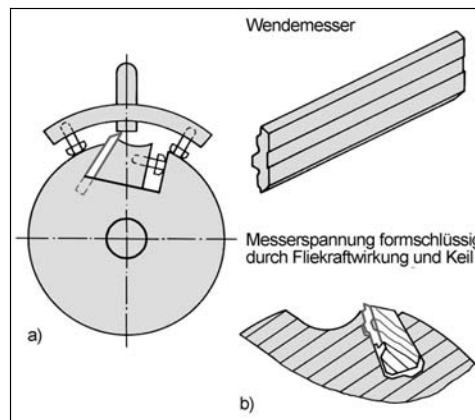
Messerwellen für Abricht- und Dickenhobelmaschine
